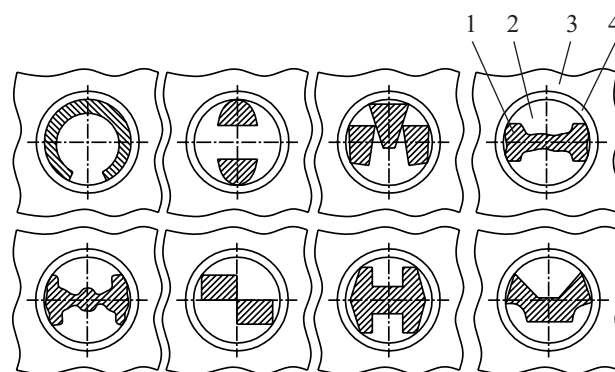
Поперечное сечение рабочей части контактов для запрессовки различной формы
